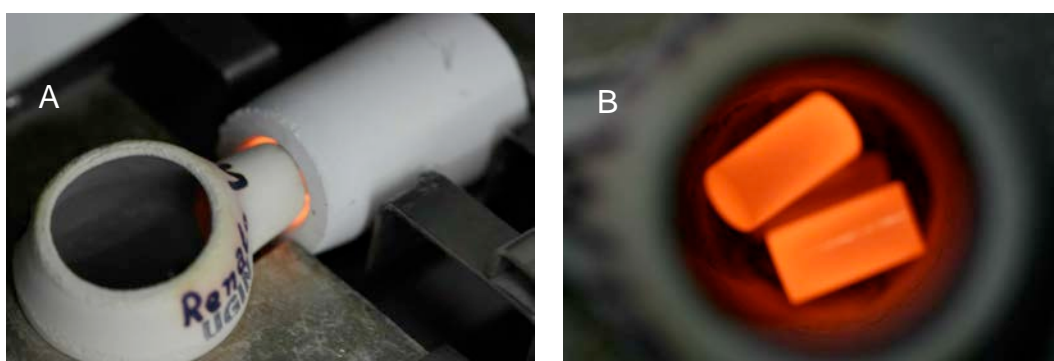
Fundição dos padrões a) máquina de indução b) fundição da liga
